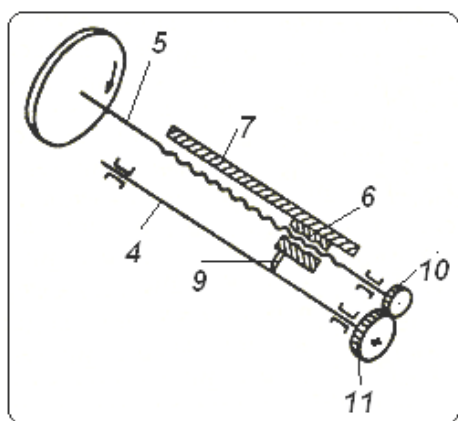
Токарно-винторезный станок с неподвижным инструментом:
